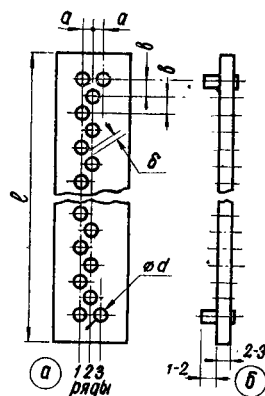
Кондуктор для сверления отверстий в решетке: а — чертеж кондуктора; б — направляющие штырьки.
